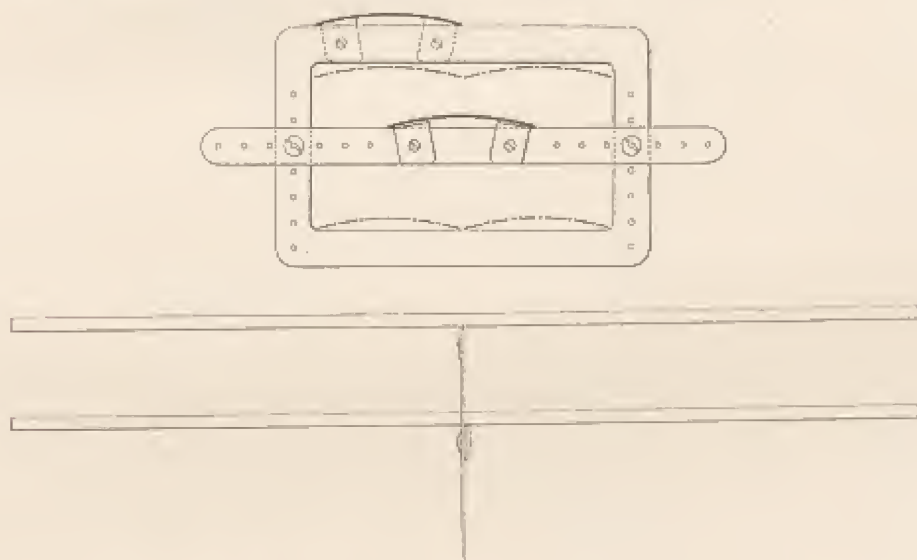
Montage des biplans : vue de profil et vue de face.
